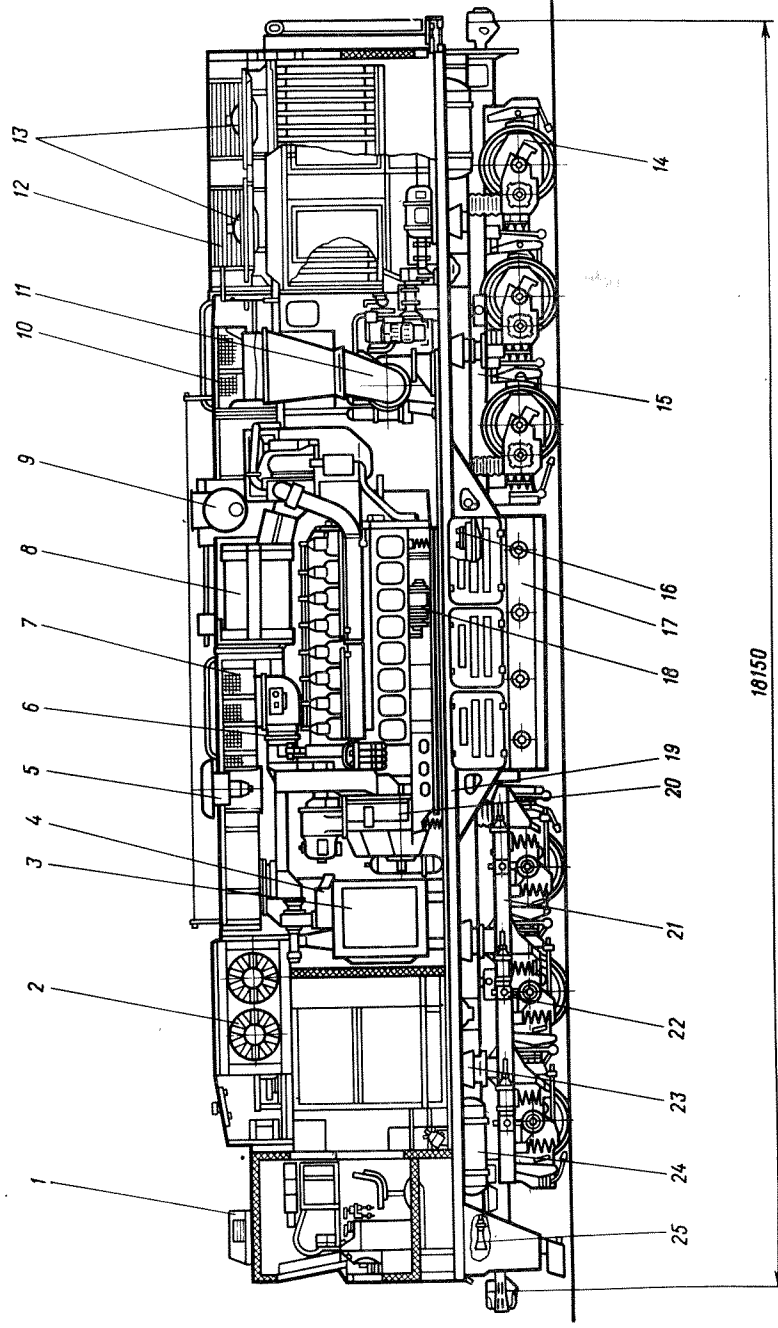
Тепловоз ТЭП116, продольный разрез и план:
